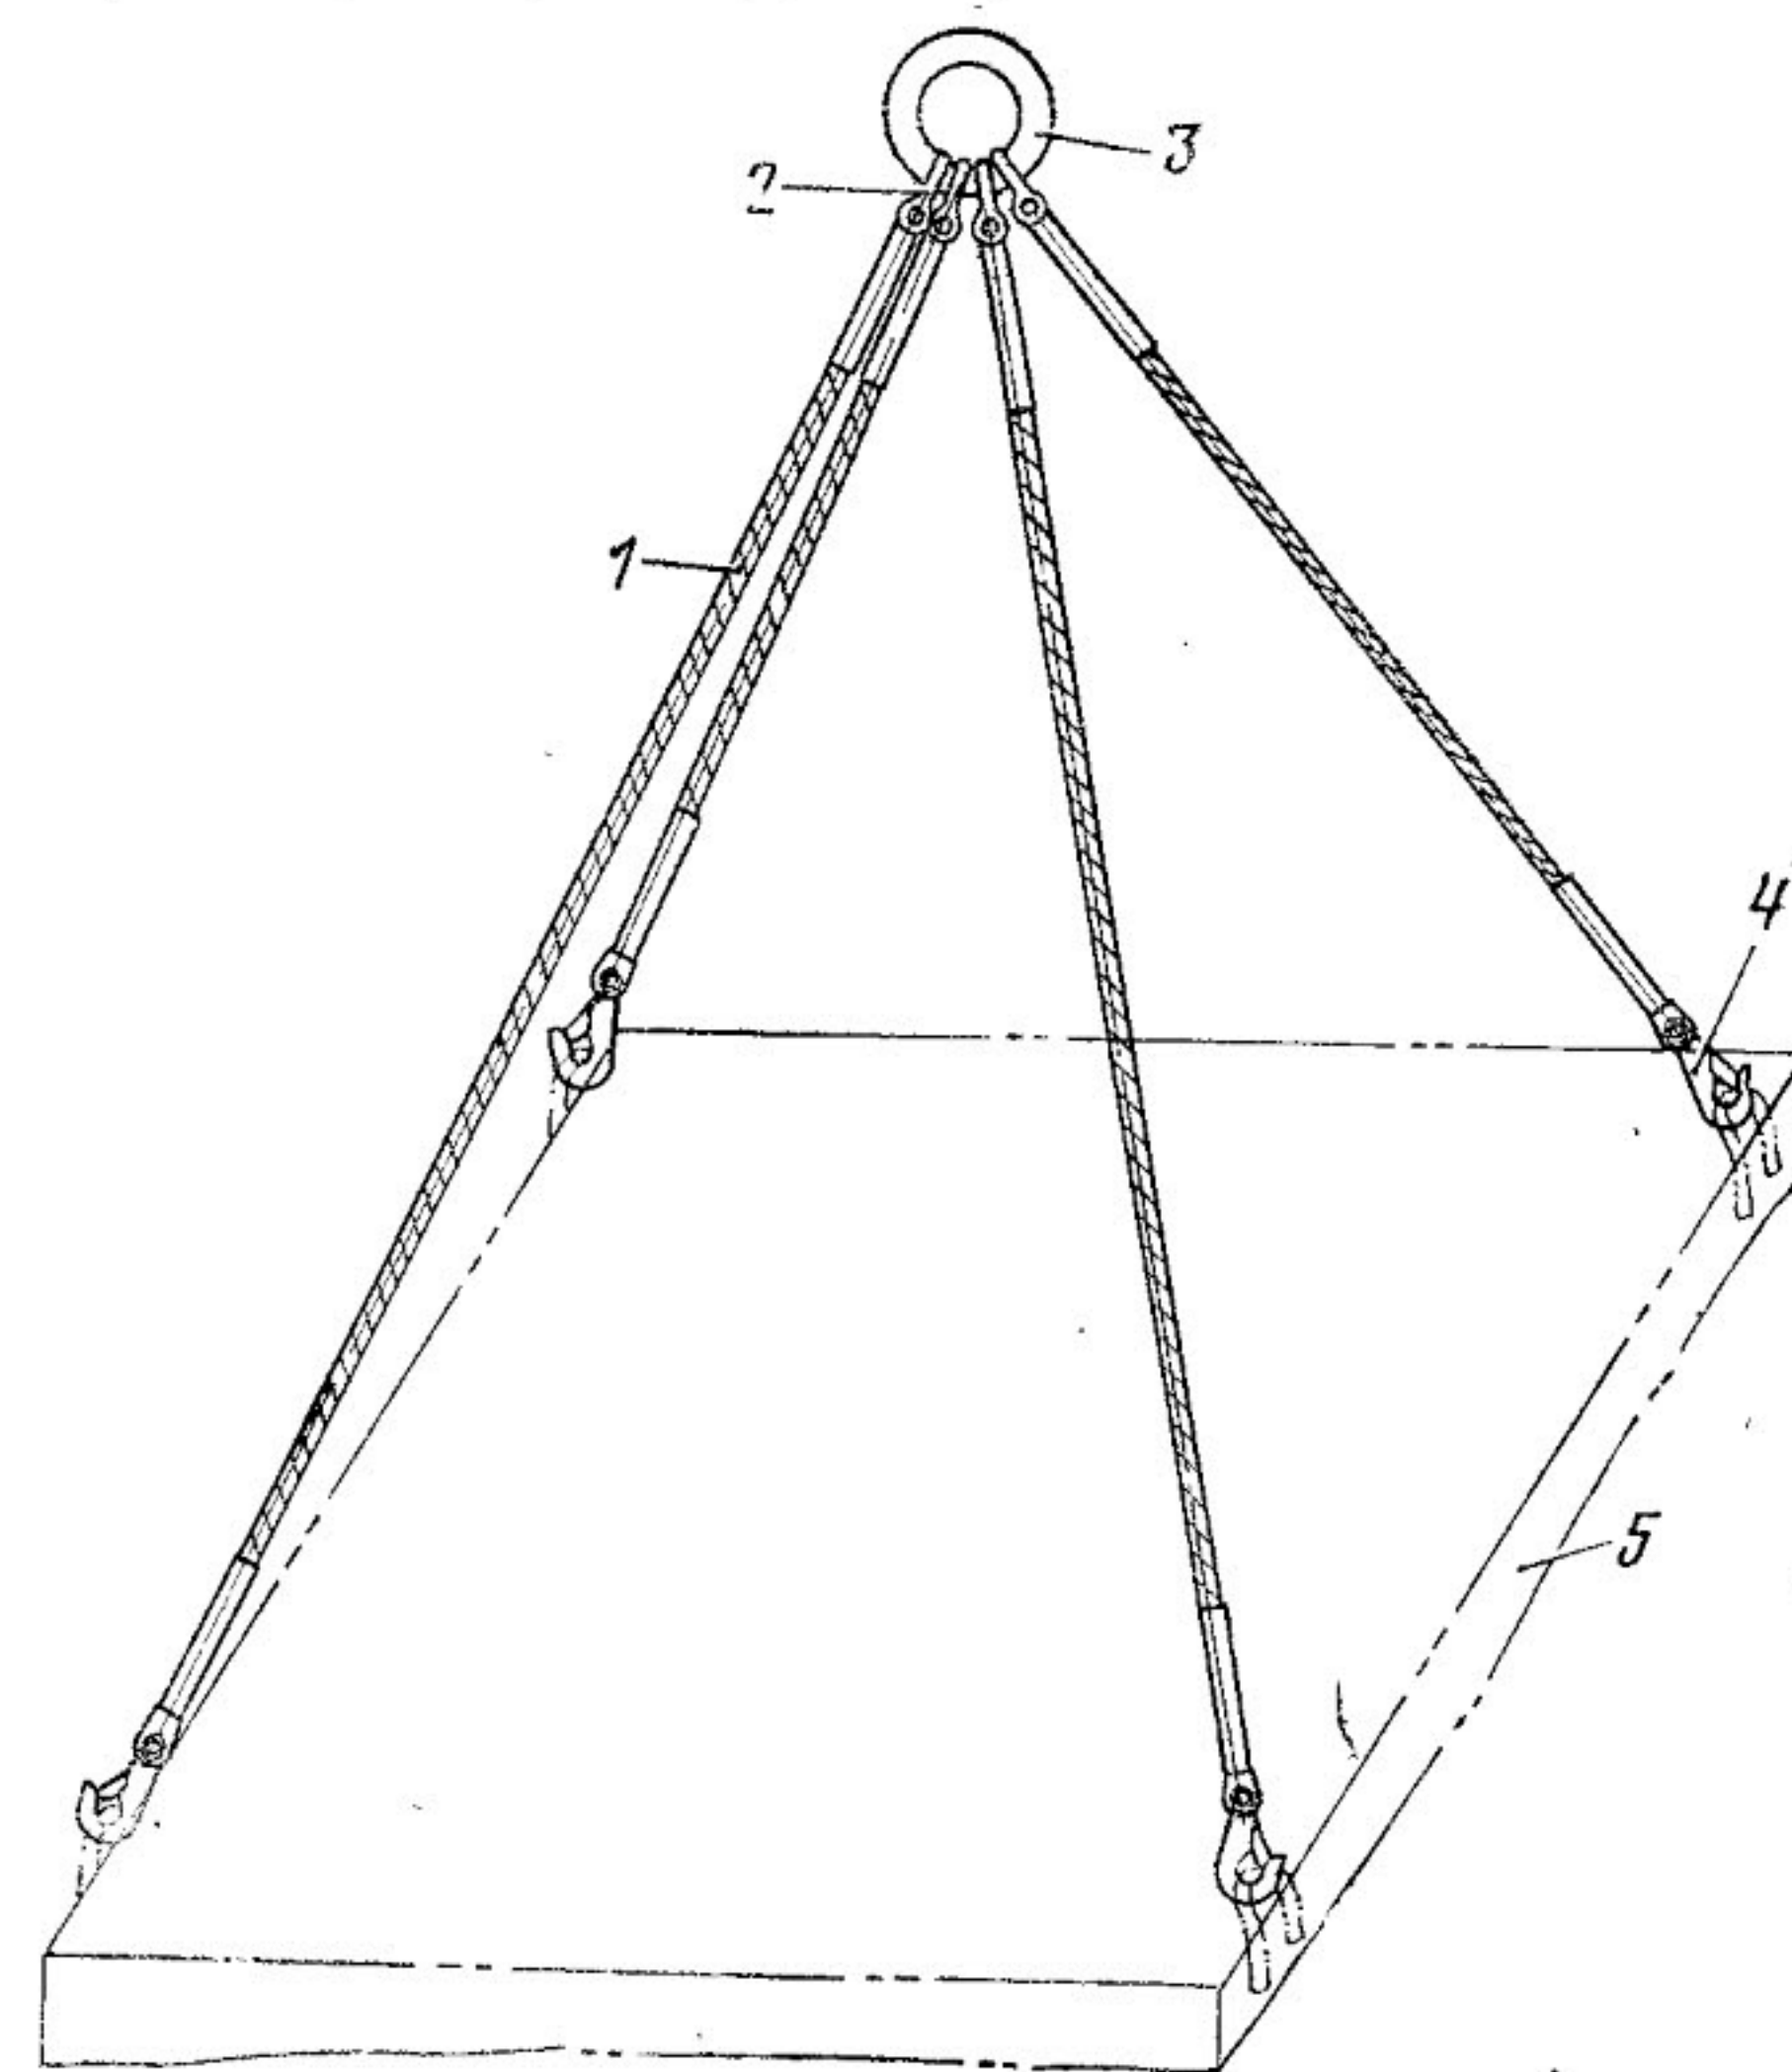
Стропы для подъема редуктора Р-7 и двигателя в контейнерах:
